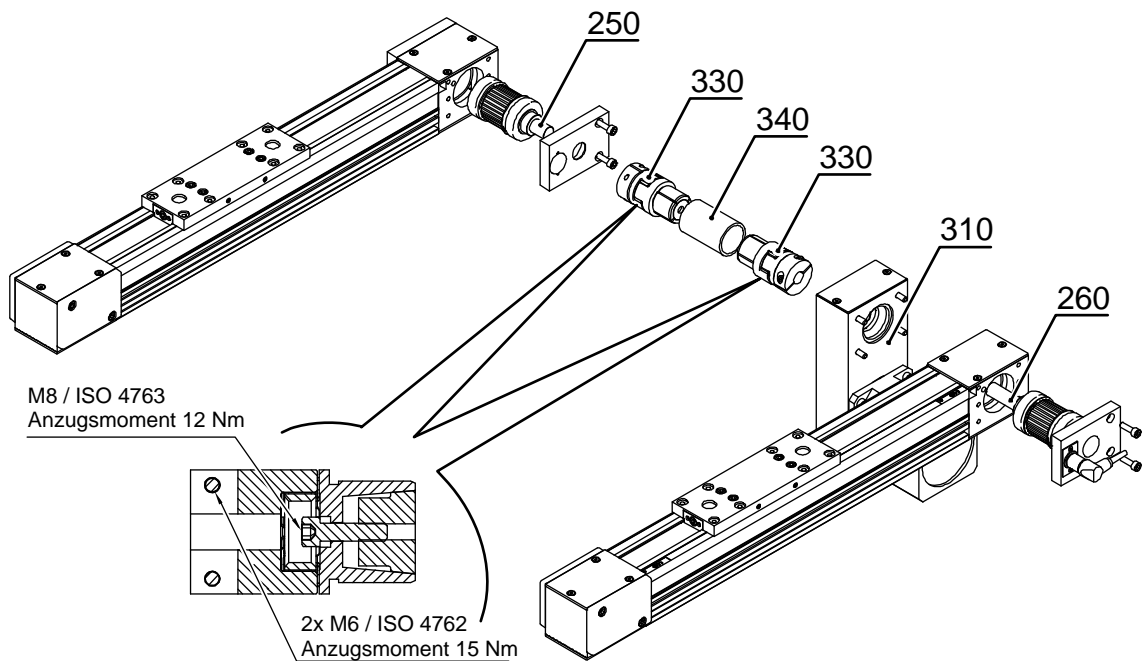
Modul 65/15, Parallel, Explosionszeichnung, Teilegruppen-Nr.: 1001028
